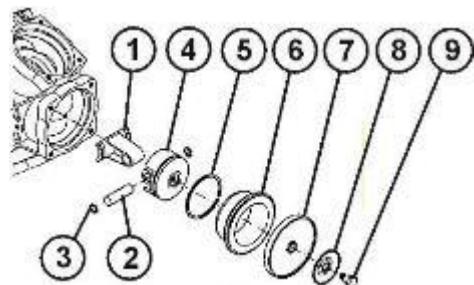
/1 Beschreibung der Pumpe - Zylinder
